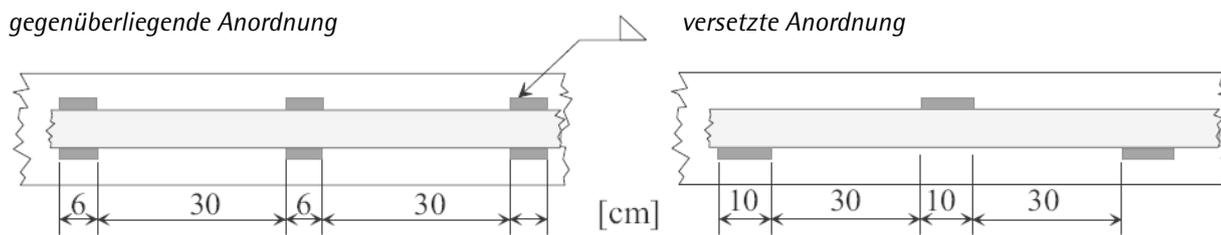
Beispiele für nicht durchlaufende Schienenschweißnähte (Draufsicht)
